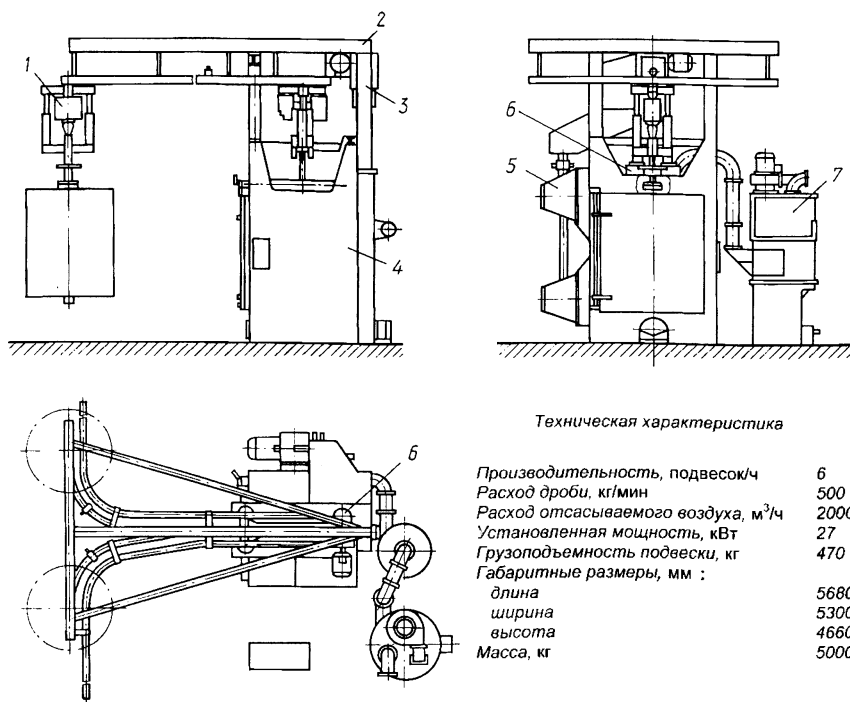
Установка дробеметная: 1 — подвеска тельфера; 2 — путь подвесной; 3 — шнек-элеватор; 4 — камера; 5 — дробемет; 6 — транспортер подвески; 7 — пылеуловитель
